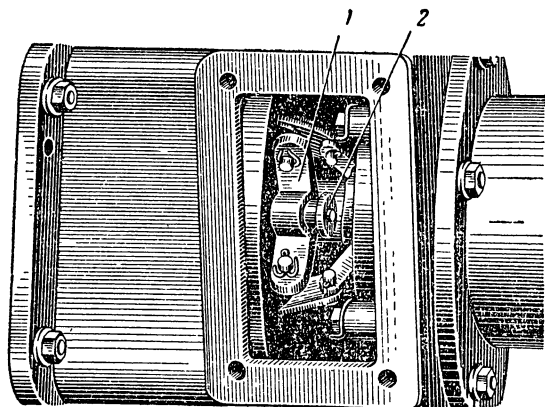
Регулировка муфты сцепления пускового двигателя:
